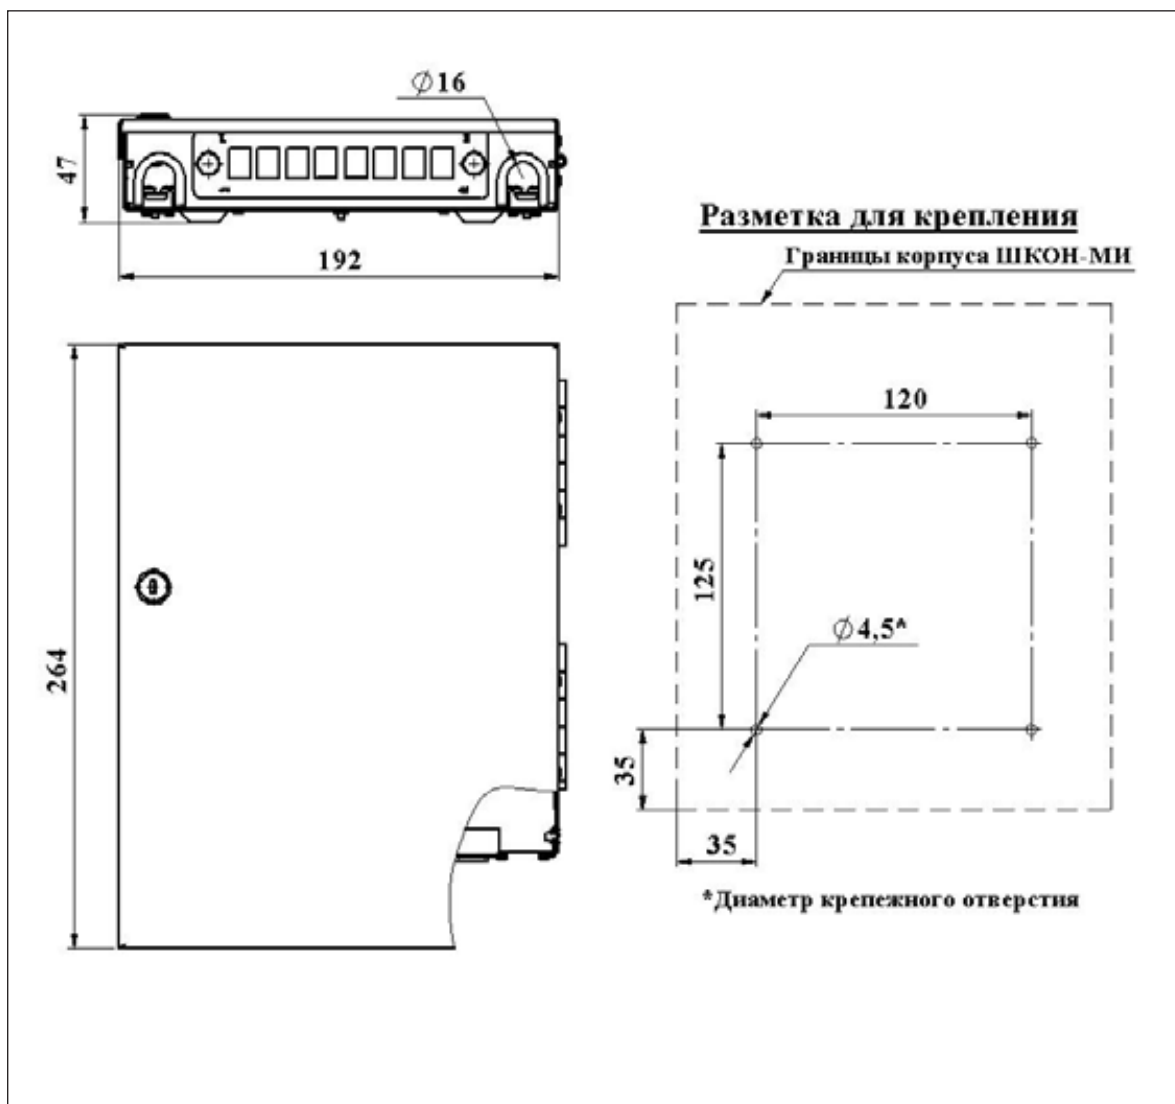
Габаритные и установочные размеры шкафа
